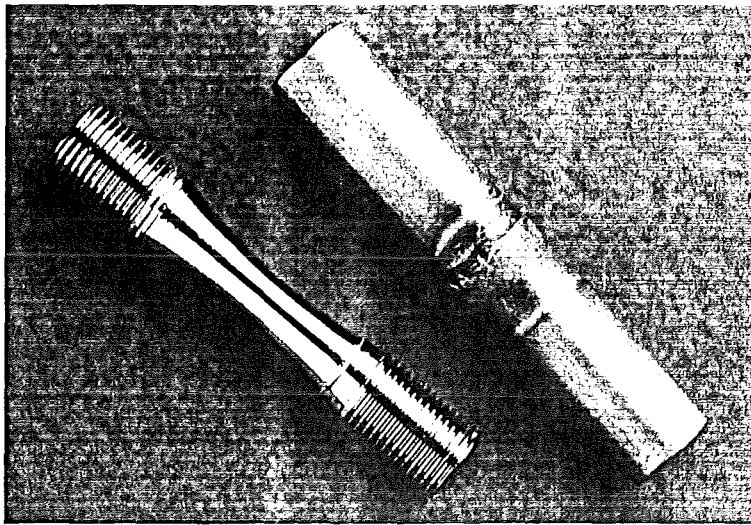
Rohling und Hourglassprobe, gedreht aus widerstandsgeschweißten 6mm-Zylindern
